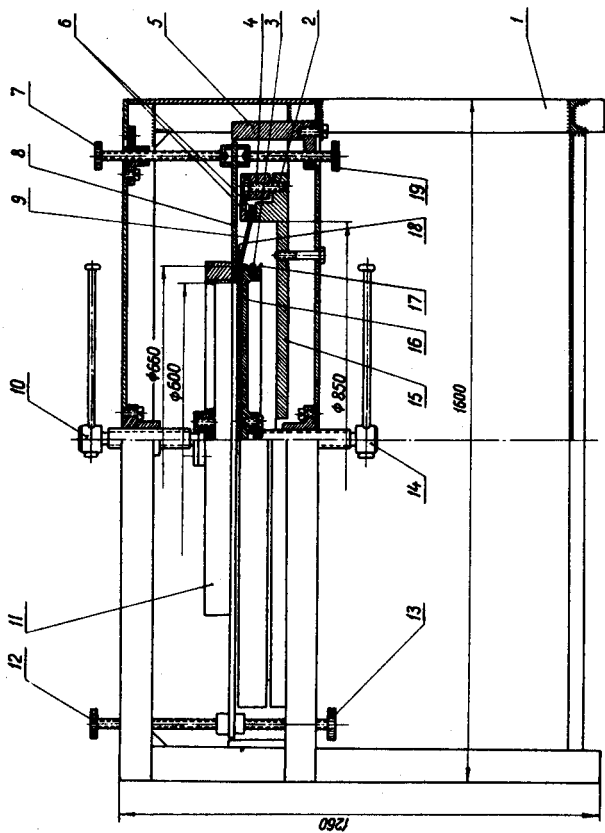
Устройство для натяжения фольги. 1 - станина; 2 - натяжной винт; 3 - резиновый шнур, крепящий прокладку из полиэтиленовой пленки 17; 4 - прижимное кольцо; 5 - контрольные уголки для центрирования электрода 8; 6 - резиновые прокладки для защемления края фольги 8; 7, 12, 13, 19 - регулировочные винты для установки положения и фиксации электрода по центру устройства; 10 - упорный винт; 11 - прижимное кольцо; 14 - винт для подтягивания пуансона 16; 15 - матрица; 18 - слой эпоксидной смолы.
